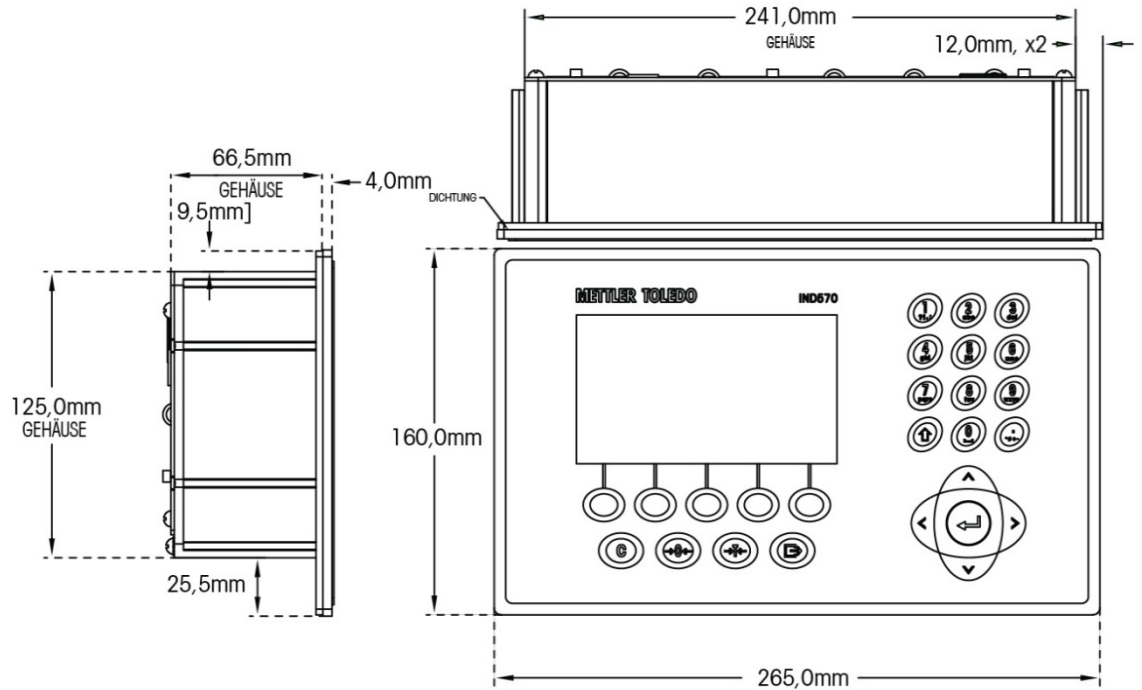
Gehäuseabmessungen der IND570-Frontplattenversion
